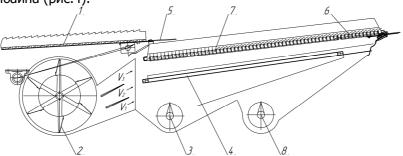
Модернизированная воздушно-решетная очистка зерноуборочного комбайна: 1 – стрясная доска; 2 - двухсекционный вентилятор; 3 – зерновой шнек; 4 – нижний решетный стан; 5 – пальцевая решетка; 6 – удлинитель верхнего решета; 7 – верхний решетный стан; 8 – колосовой шнек
